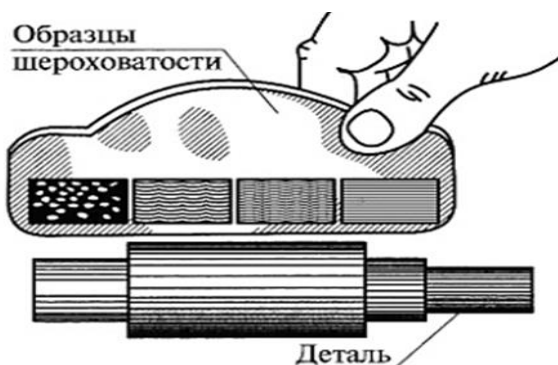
Контроль шероховатости с помощью эталонных образцов
